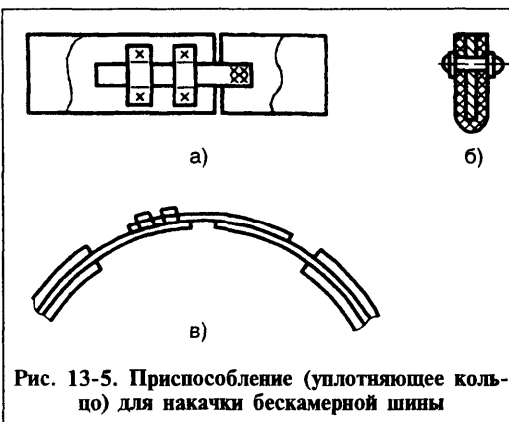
Приспособление (уплотняющее кольцо) для накачки бескамерной шины
